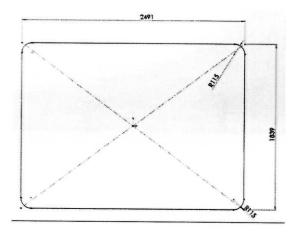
Vista en planta de dimensiones generales de la cabina
